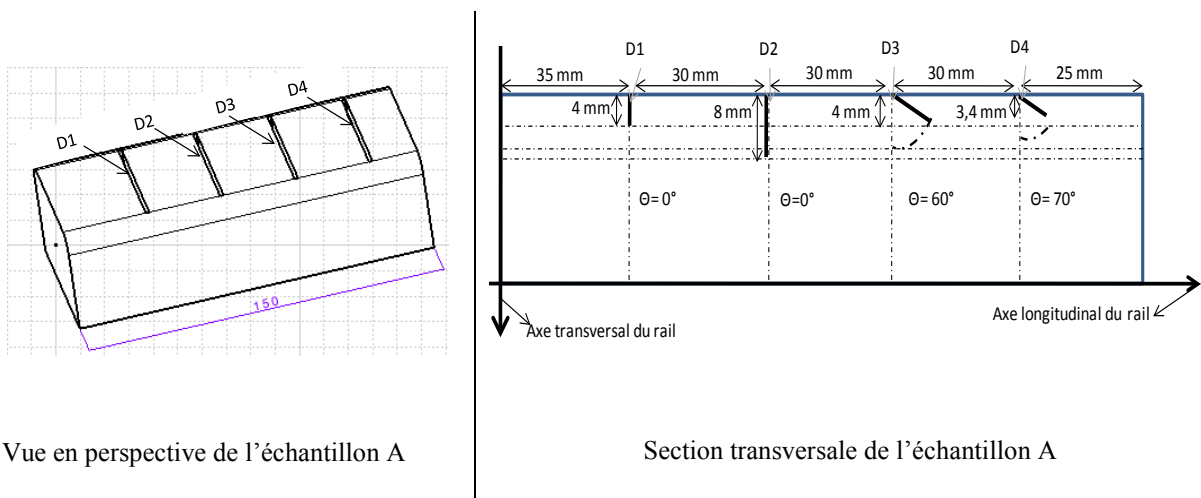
Configuration des défauts mettant en évidence les angles d'inclinaison des fissures par rapport au plan transversal du rail (θ°) (coupe transversale de la section du rail)
